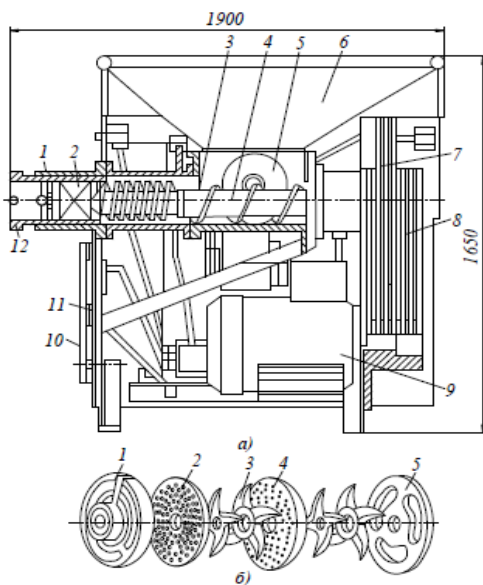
Волчок К7-ФВП-160-2: *а* – схема волчка; *б* – режущий механизм
